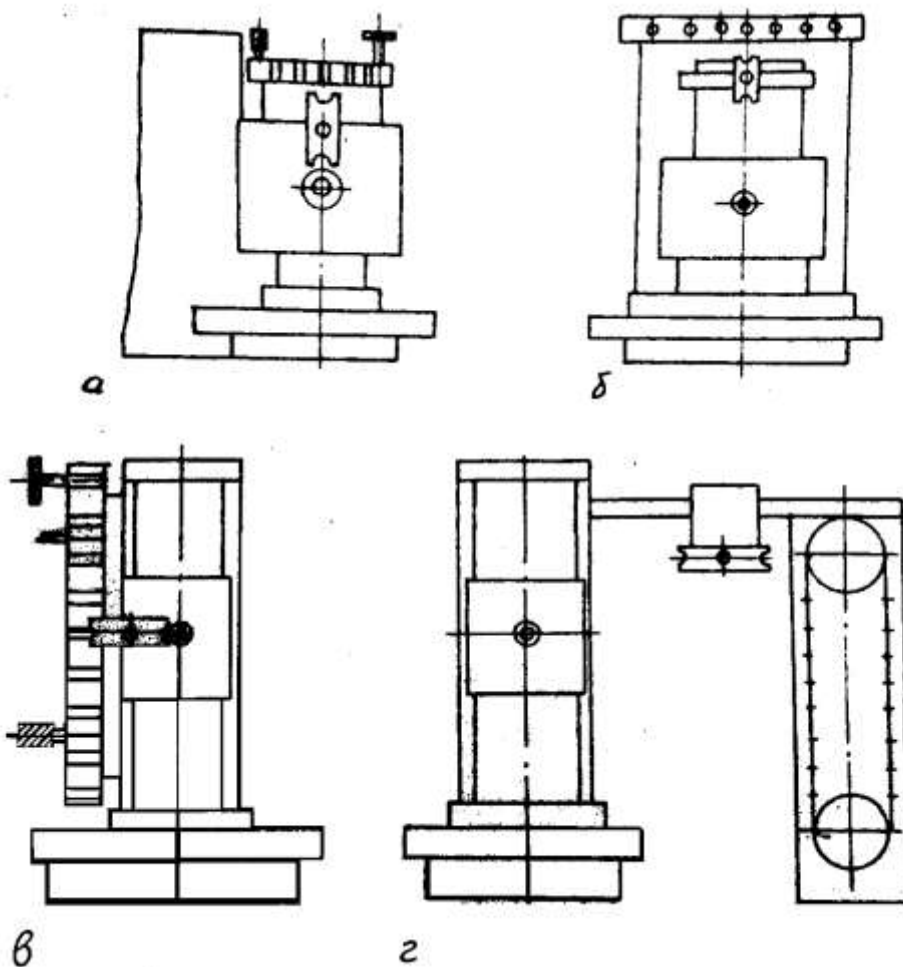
Основні схеми розташування інструментальних магазинів на багатоцільових верстатах з ЧПУ [1]
